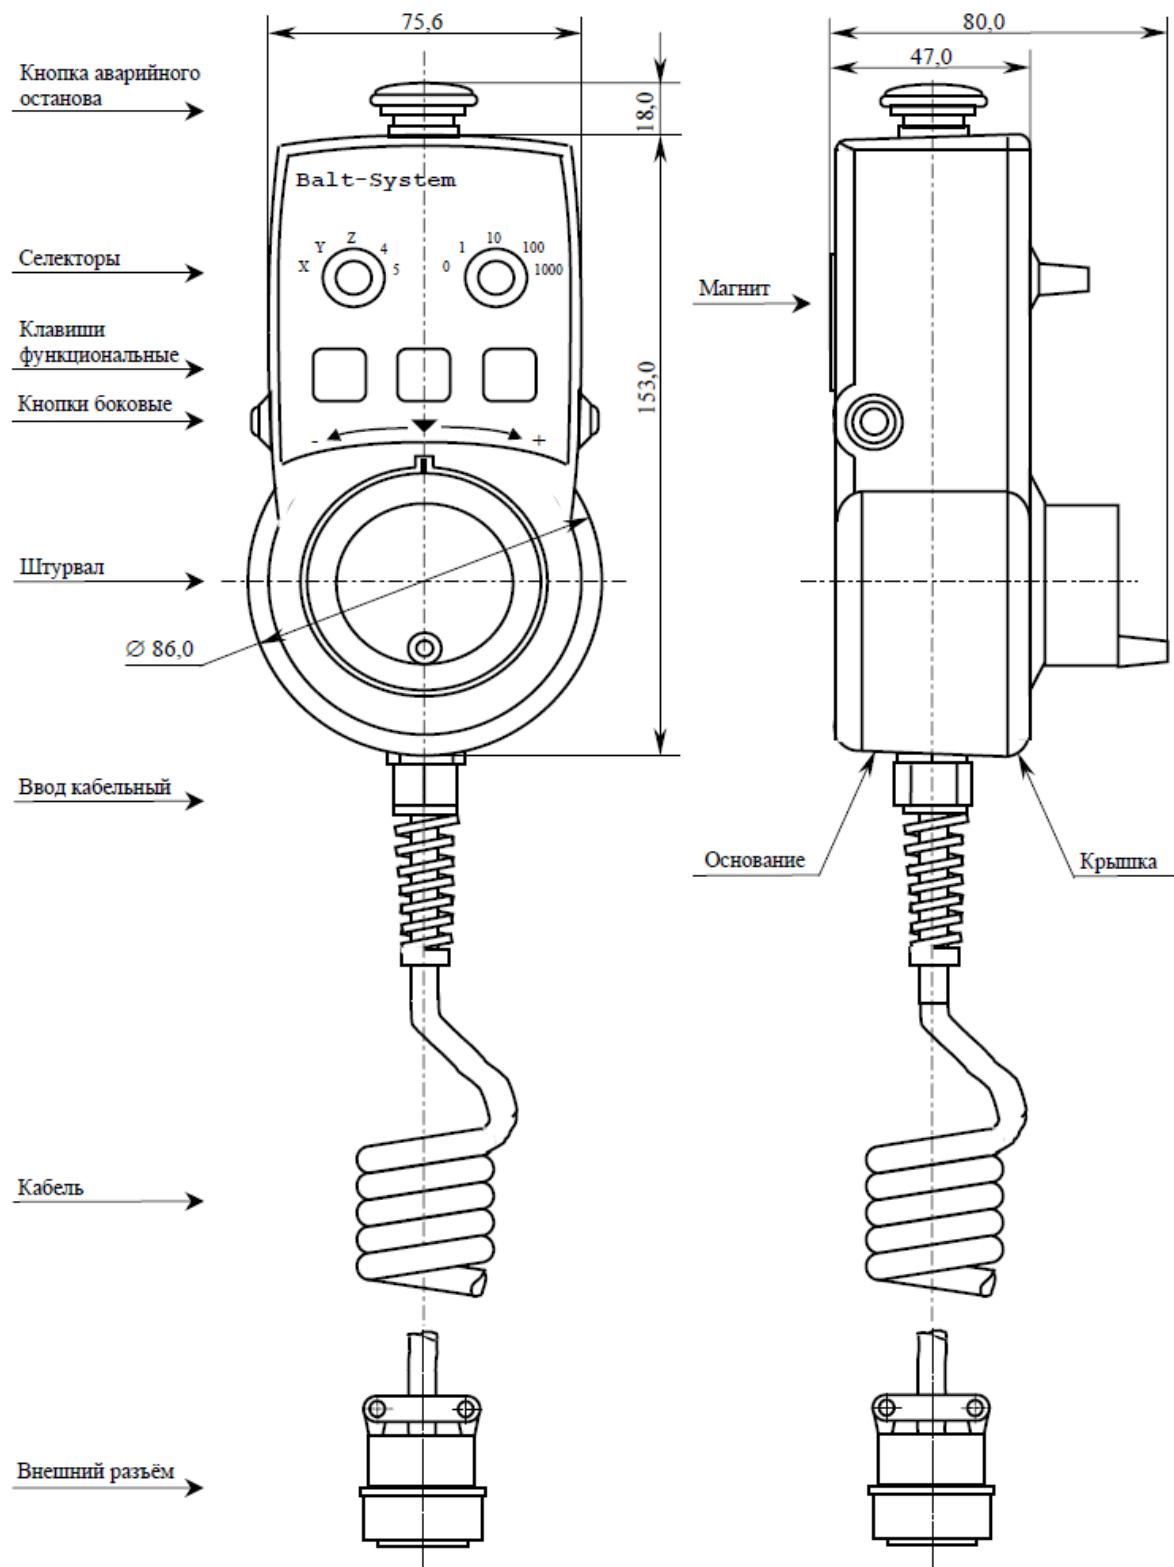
Основные размеры и расположение элементов NC 110-78B
